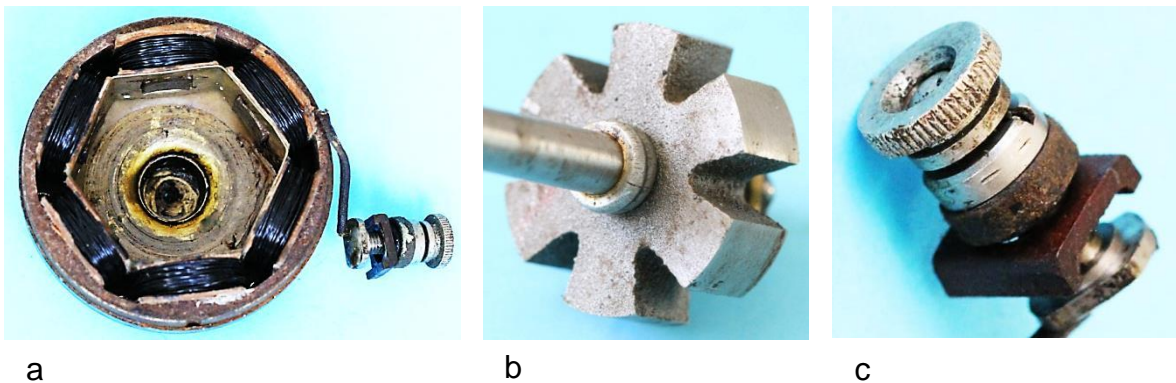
Bauteile des Generators: a) Anker mit Kabelanschlussbolzen: Durchmesser des Ankerblechpakets 66,5 mm , axiale Länge 9,5 mm (19 Bleche), b) Massives Polrad, c) Kabelanschlussbolzen
